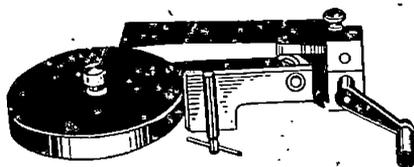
Машинка ручная для окантовки чертежей «ОКМ-3»
